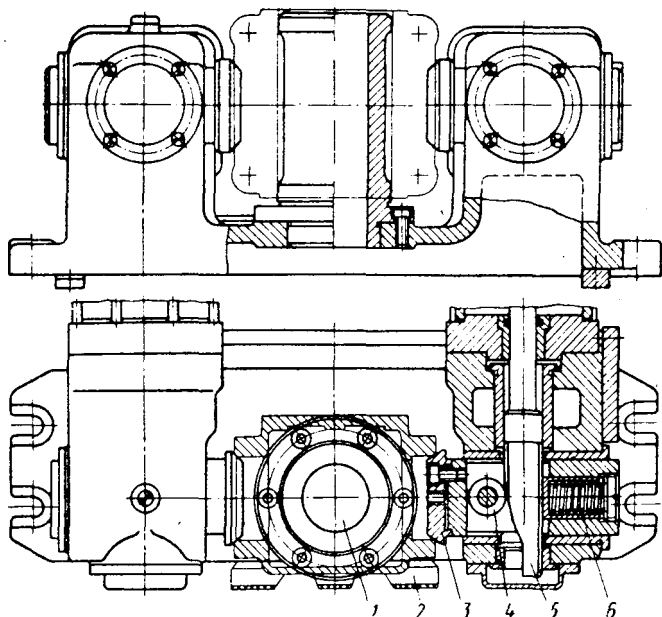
Приспособление для фрезерования опорной плоскости в корпусных деталях
